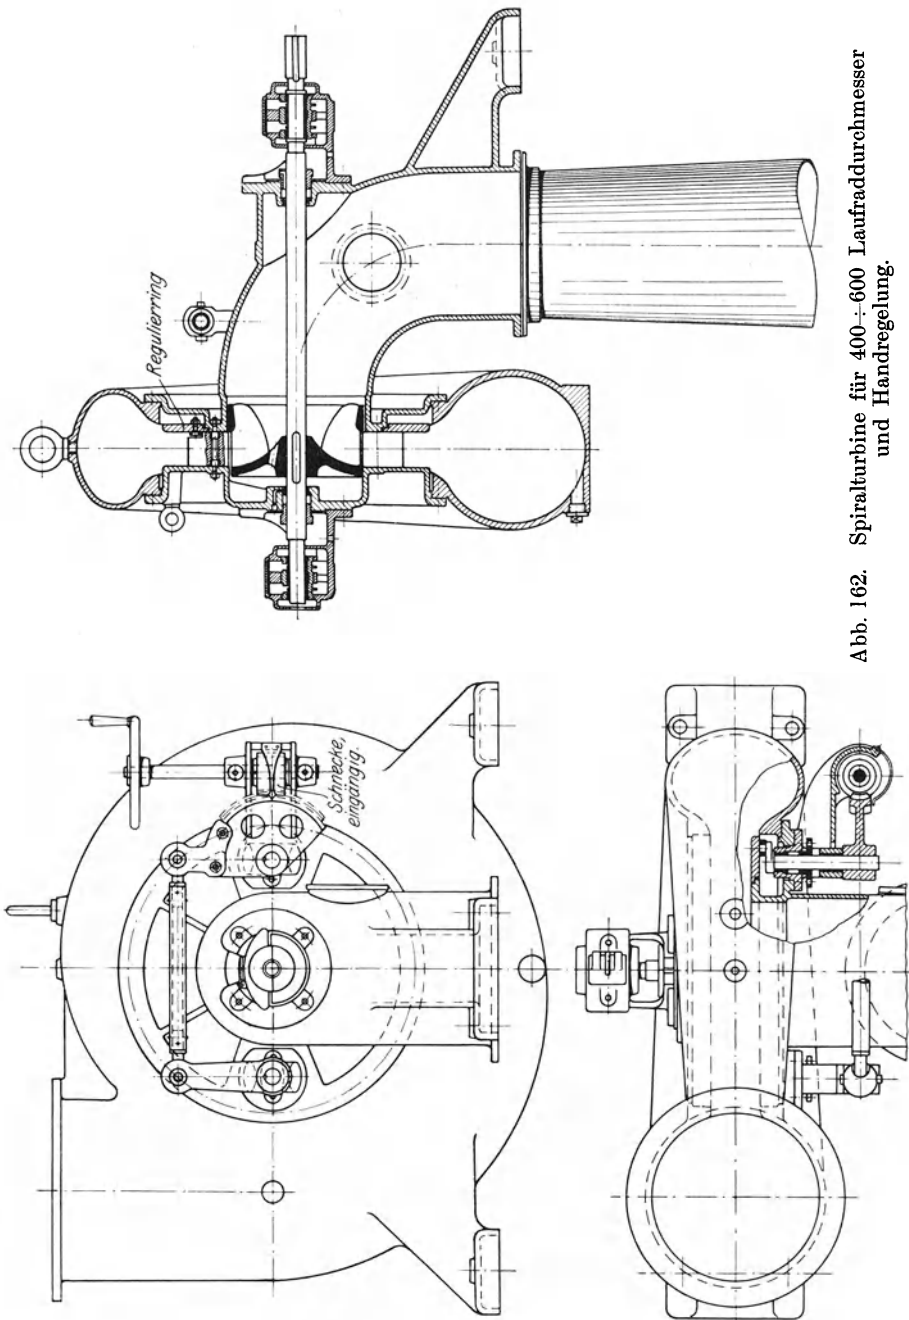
Spiralturbine für 400--600 Laufdurchmesser und Handregelung.
